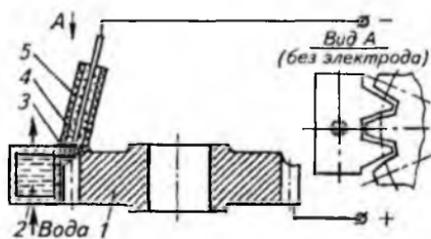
Схема наплавки торцов зубьев под флюсом:
